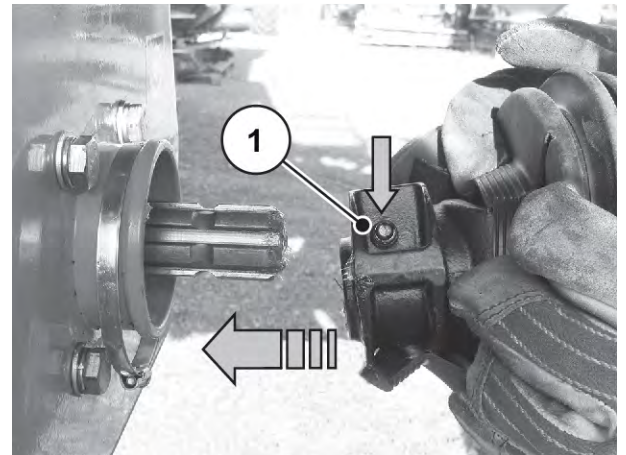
Gelenkwelle auf Getriebezapfen aufstecken
